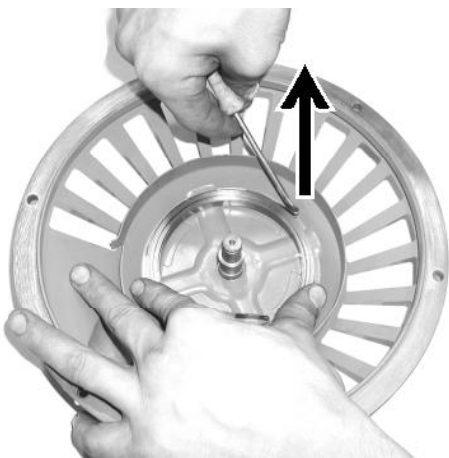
Вытаскивание пружины из корпуса стартера
